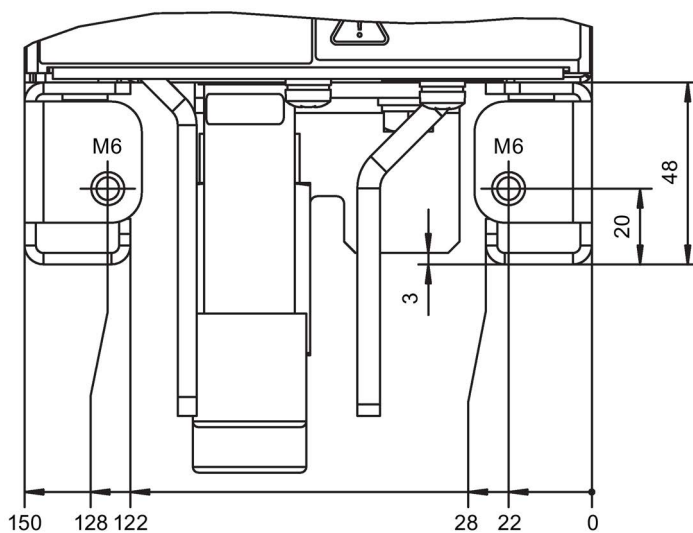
Сечение шины активного модуля питания и модуля двигателя, типоразмер GXL (размеры указаны в мм)
